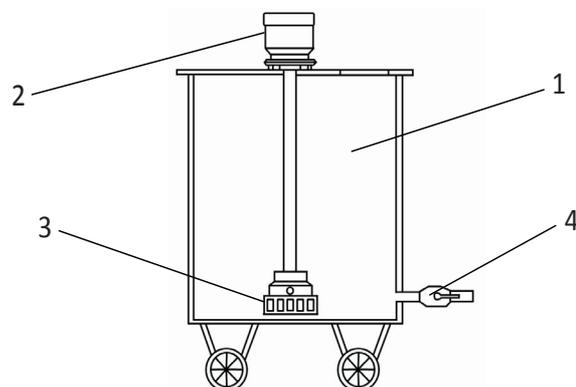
Схема агрегата для приготовления заменителей молока роторным диспергатором:
